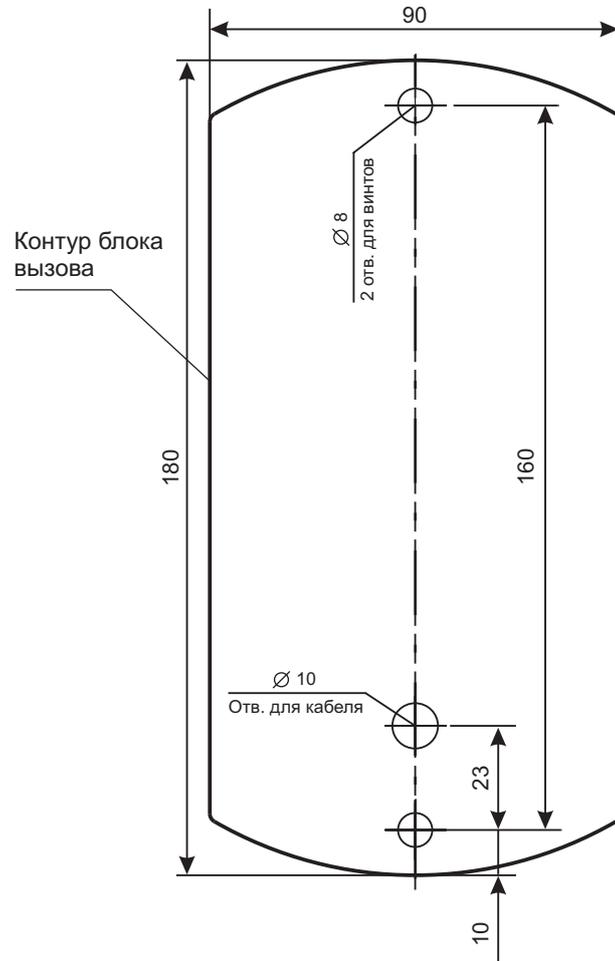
Расположение и размеры отверстий для установки блока вызова
